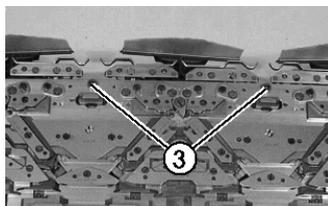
Schrauben für Gusskörper an der Schlossplatte
